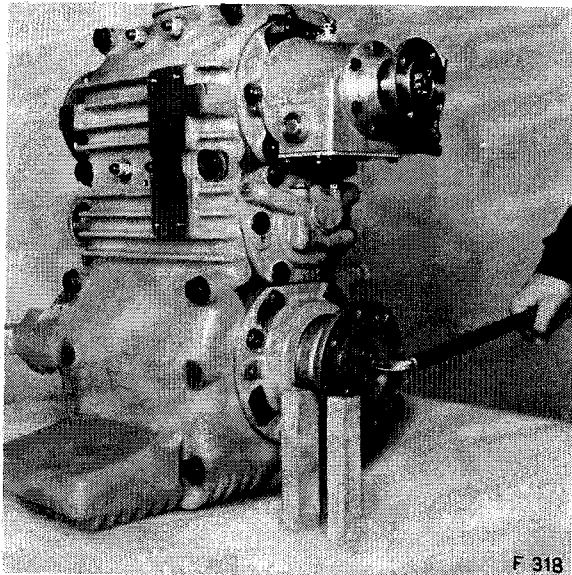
Lösen der Befestigungsschrauben des Antriebsflansches für die Hinterachse
